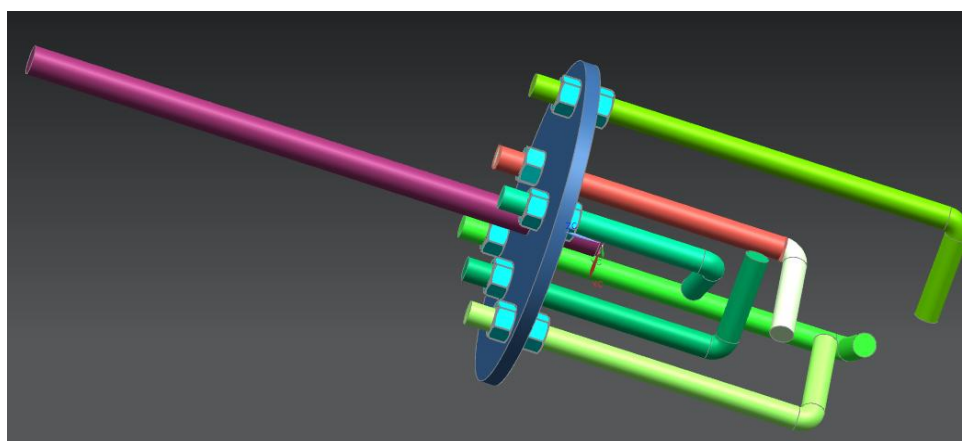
Модель сборки ротора (повернуто на 70°)
